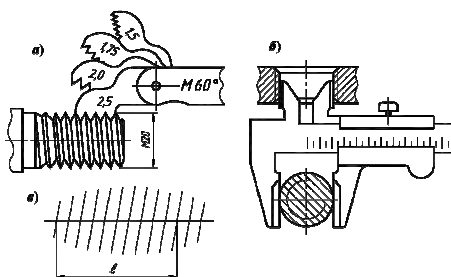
Контроль параметров резьбы : а- шаблон профиля резьбы; б- диаметра; в- шага резьбы
